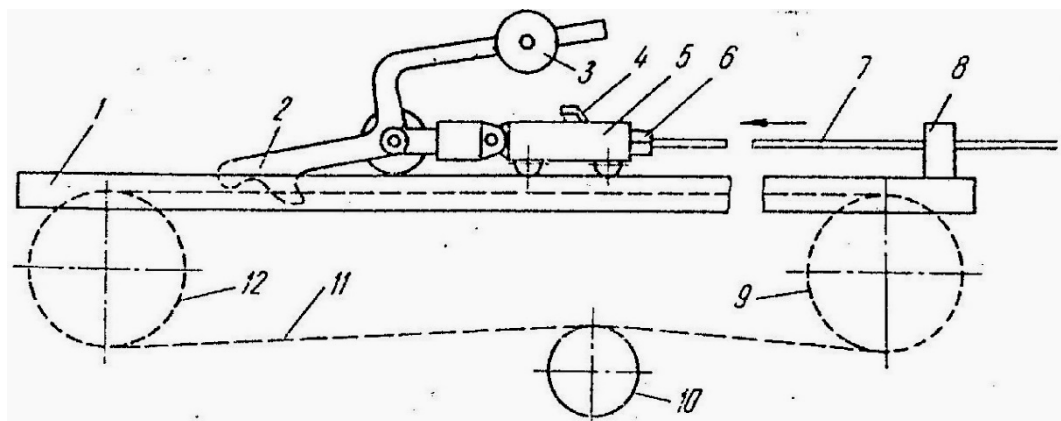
Схема процесу волочіння на ланцюговому стані: 1 - станина; 2 - крюк для захвату ланцюга; 3 - контрвантаж; 4 - 6 - кліщовий пристрій; 7 - пруток; 8 - волока; 9 - ведена зірочка; 10 - натяжний ролик; 11 - ланцюг; 12 - приводна зірочка
